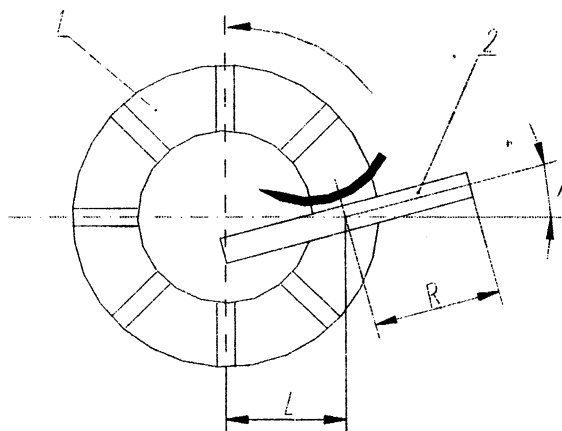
Кинематическая схема обработки пазов на торце детали
